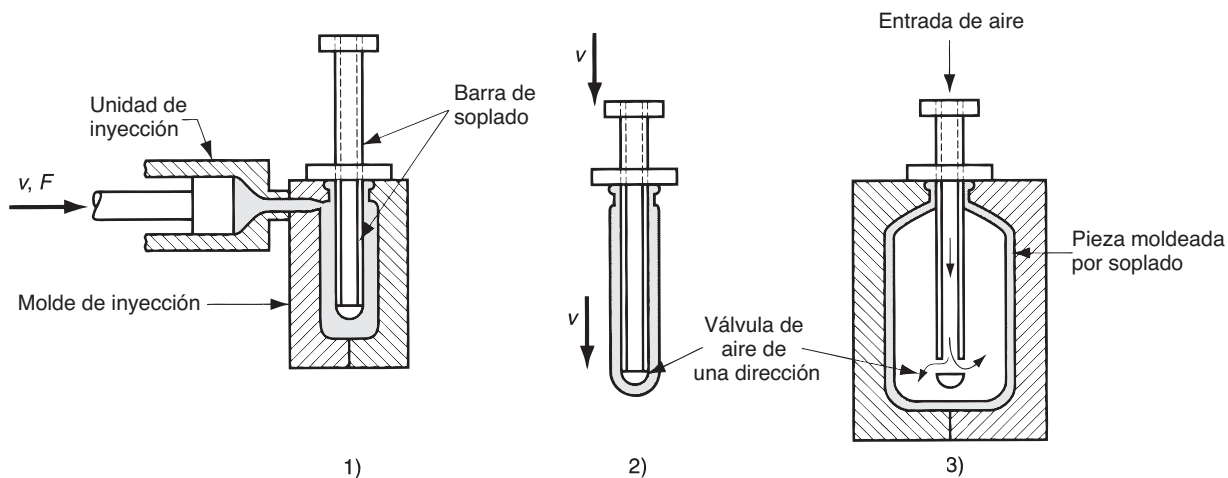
Moldeo soplado por estiramiento: 1) moldeo con inyección del parison, 2) estiramiento y 3) soplado.
